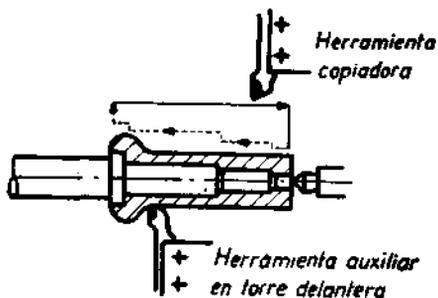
Ejemplo de copiado de forma, pieza con sobre-espesores de estampado, con herramienta auxiliar de desbaste en la torre delantera.
